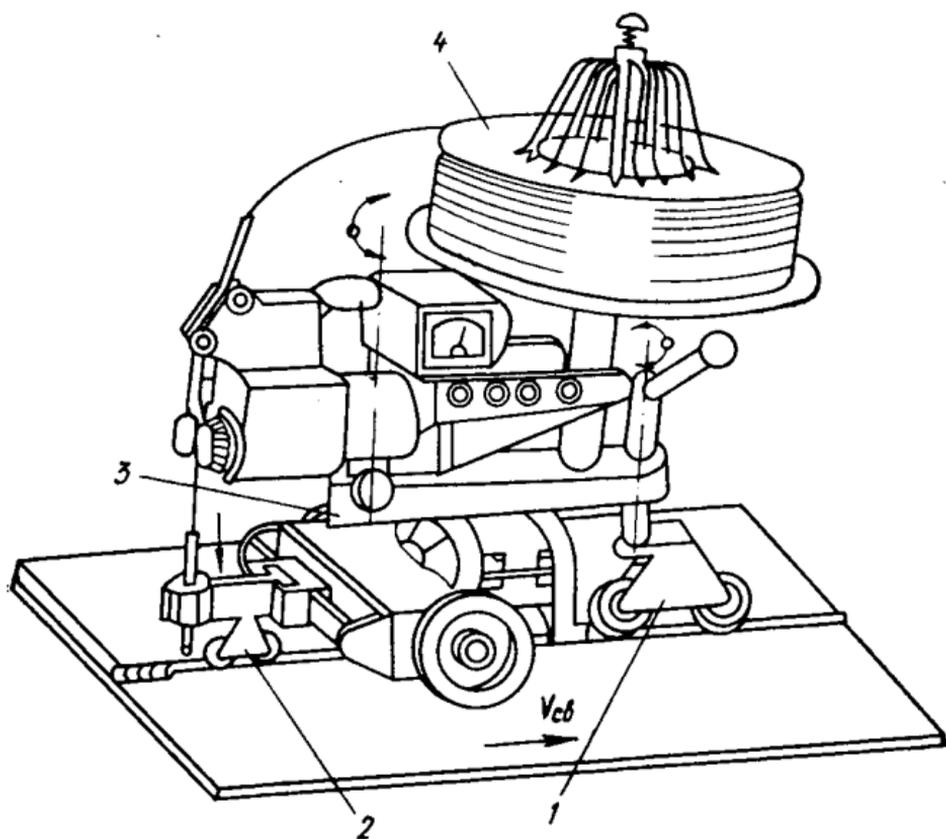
Приставка модели г-2 к сварочному трактору ТС-35 для сварки соединений внахлестку:
